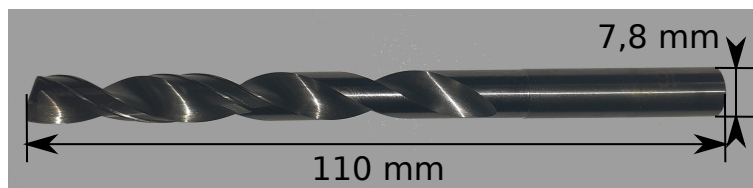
Foret hélicoïdal en carbure monobloc pour perçage sur machine UPA
